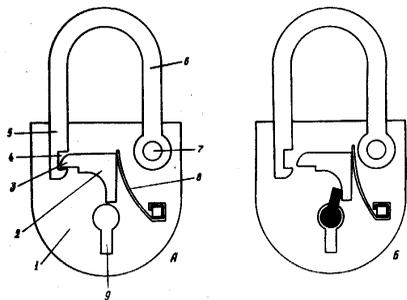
Устройство навесной пружинный замок: 1 — дно корпуса замка; 2 — засов; 3 — запирающая головка засова; 4 — запираемый вырез дужки; 5 — запираемый конец дужки; 6 — дужка замка; 7 — ось крепления дужки; 8 — пружина; 9 — скважина для ключа.
